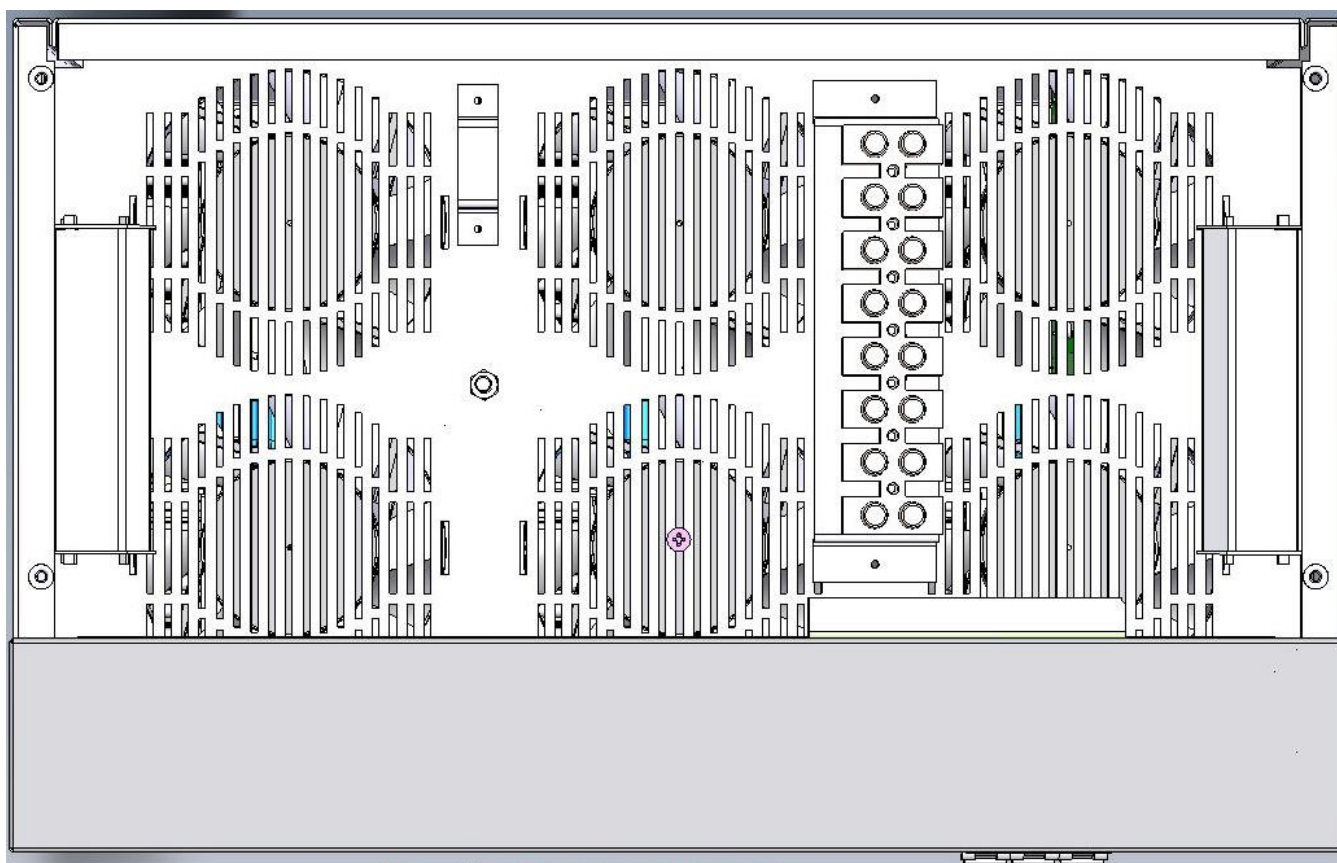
Внешний вид верхней части стабилизатора без крышки
